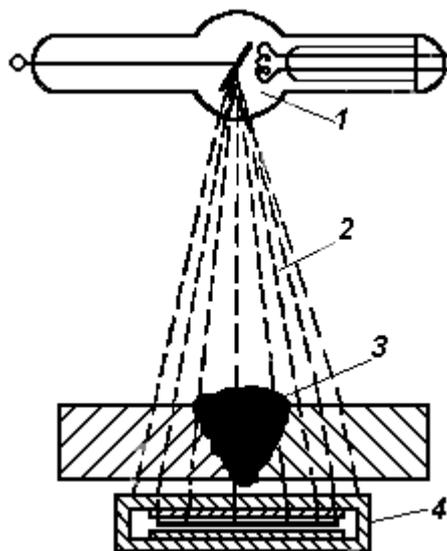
Рентгеновское просвечивание сварного шва:
